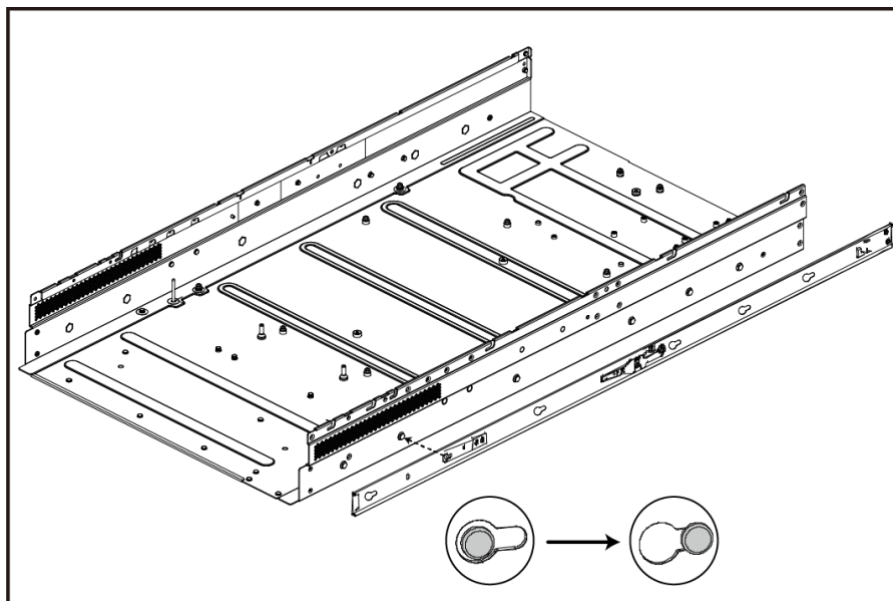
Установка внутренних подвижных рельс на корпус сервера
